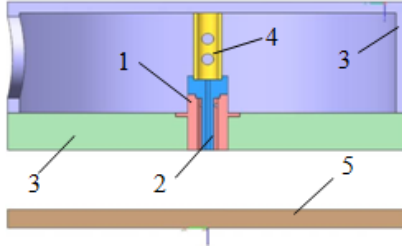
Исследуемая модель: 1 – закручивающее устройство; 2 – центральное сопло; 3 – стенки камеры нагнетания; 4 – вставка; 5 – исследуемая стенка
